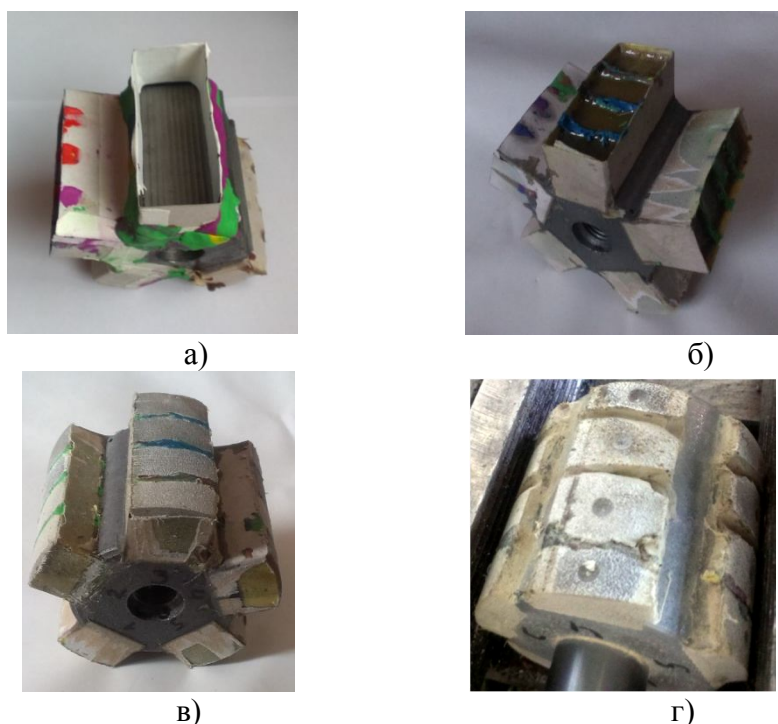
Подготовка образца к испытаниям: а – форма; б – образец с отвержденными композитами; в – образец после механической обработки - точения; г – образец с высверленными лунками
